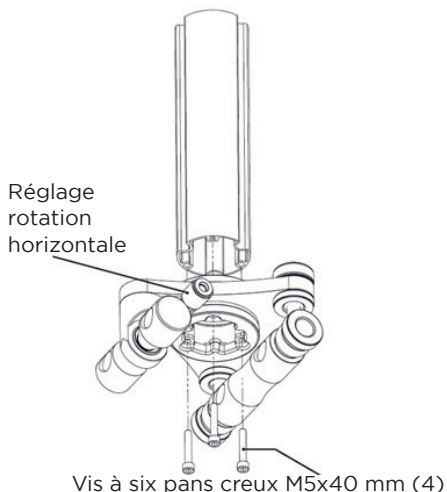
Assemblage du tube télescopique et de la plaque de montage
